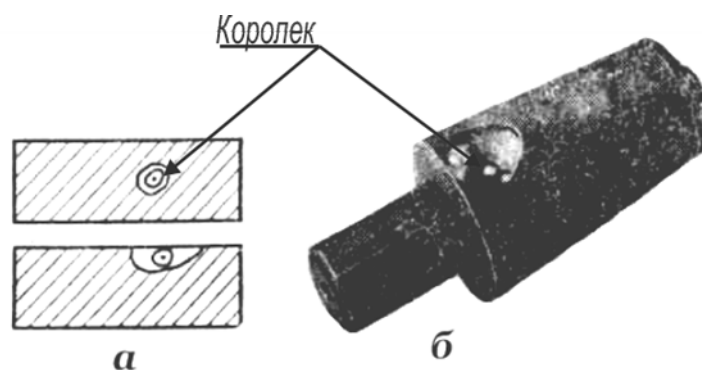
Дефект – королек: а – схема; б – дефектная отливка
